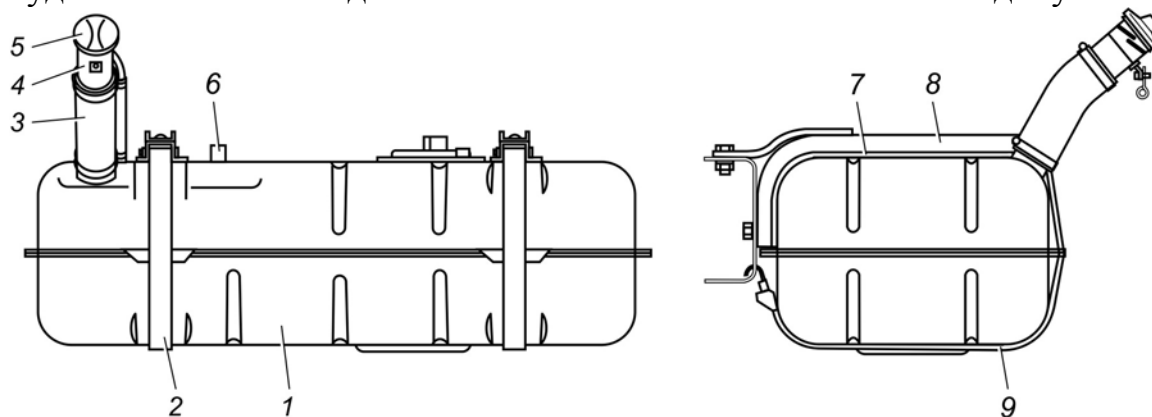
Топливный бак: 1 – топливный бак; 2 – хомут; 3 – шланг наливной трубы; 4 – труба наливная; 5 – пробка; 6 – клапан бака; 7 – прокладка под кронштейн; 8 – кронштейн; 9 – прокладка
